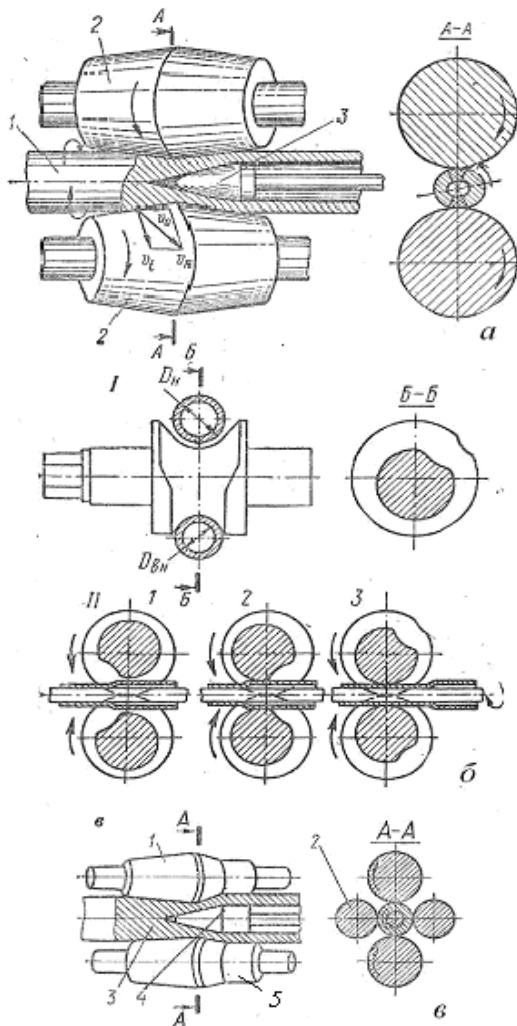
Трубопрокатні стани: *а*-прошивний (1-заготовка; 2-конусні валки; 3-прошивка); *б* – пілігримовий (1-положення гільзи в момент подачі її в калібри валків, 2-період початку прокатування, 3-період кінця прокатування труби); *в*-автоматичний (1-конусні прокатні валки; 2-підтримуючі валки; 3-заготовка; 4-прошивка; 5-циліндричні хвостовики валків
